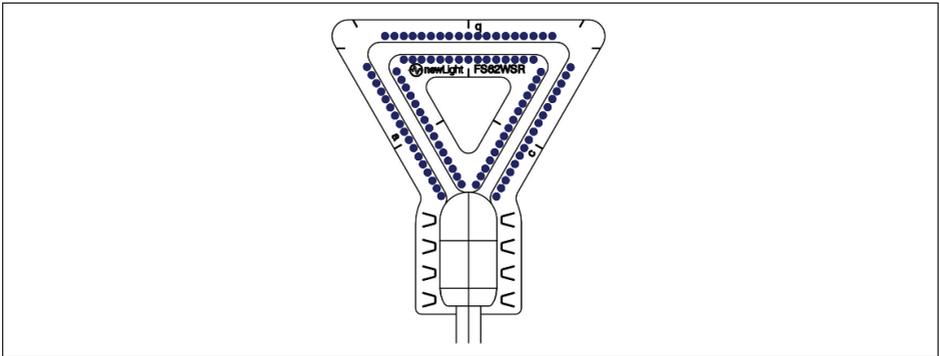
Schweißreihenfolge für die Rosette FS62WSR, Schritt 2
